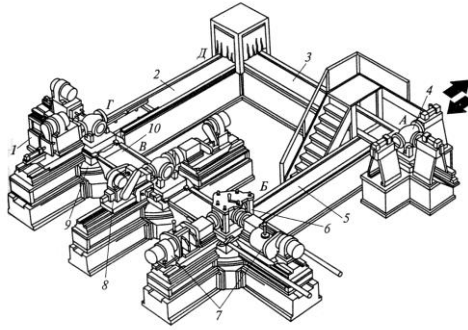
Однопредметна автоматична лінія для обробки корпусу клапана з пристосуванням-супутником: 1, 7, 8 - верстати; 2, 3, 5, 10 - крокові конвеєри; 4 - оброблена деталь; 6 - ПС; 9 - стіл; А - позиція контролю і завантаження-вивантаження; Б, В, Г, Д - робочі позиції
